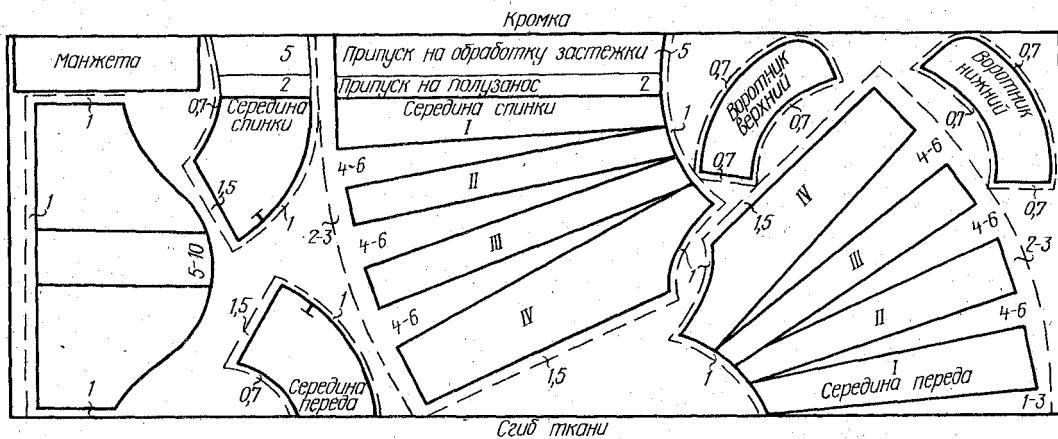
Раскладка выкроек на ткани и раскрой платья на круглой кокетке
